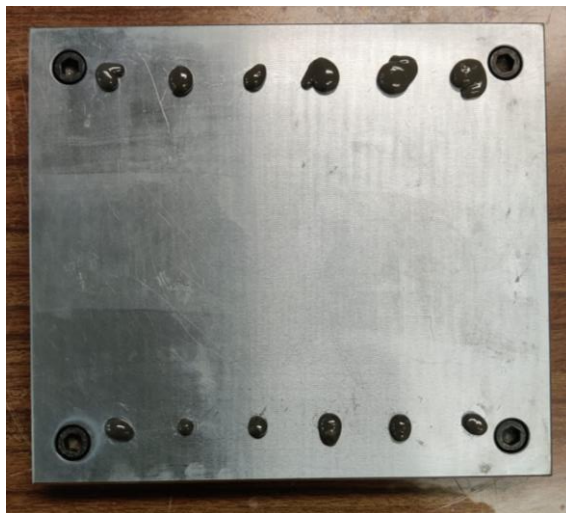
Fecho do molde e surgimento de excesso de adesivo
